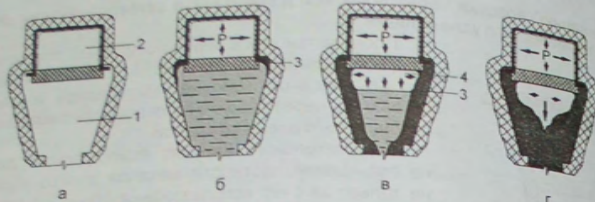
Схема затвердевания расплава в прибыли воздушного давления:
